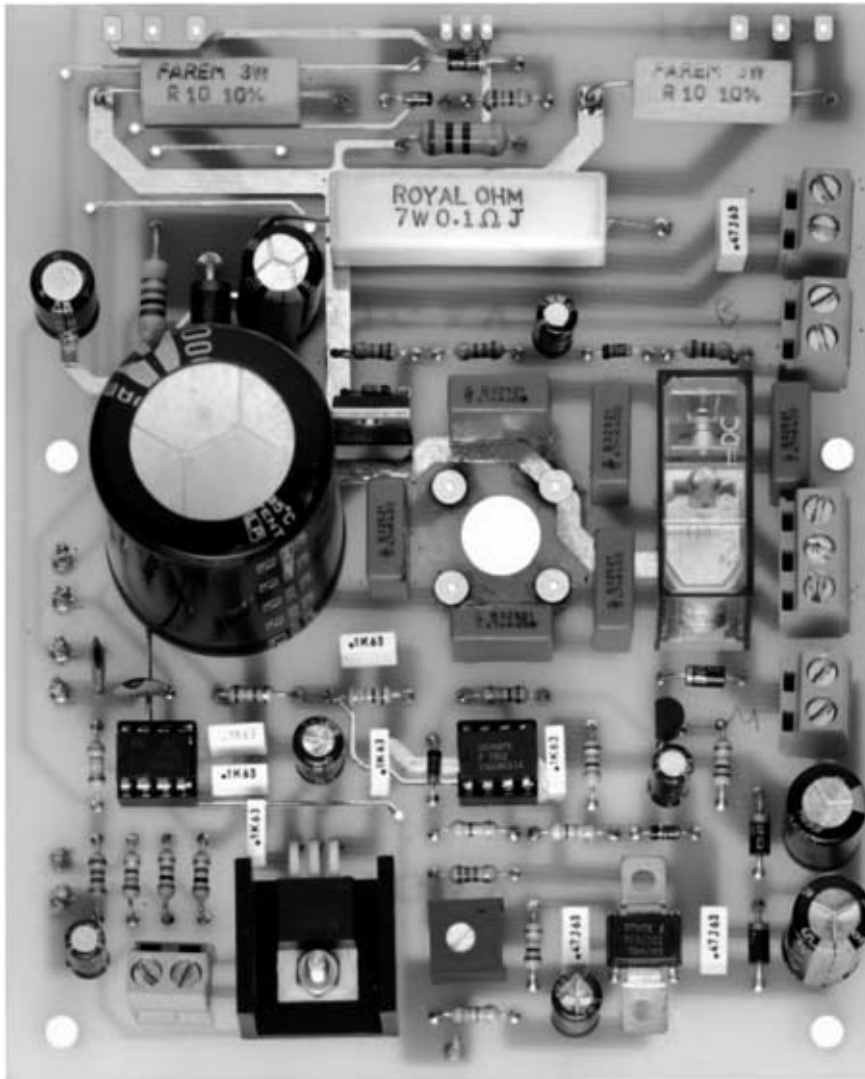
Fotografía del circuito impreso LX.1643. En la parte inferior-izquierda se puede observar el integrado estabilizador L7805 montado en posición horizontal sobre su pequeña aleta de refrigeración. El trimmer situado a la derecha del integrado L7805 se utiliza para ajustar el Alimentador.
